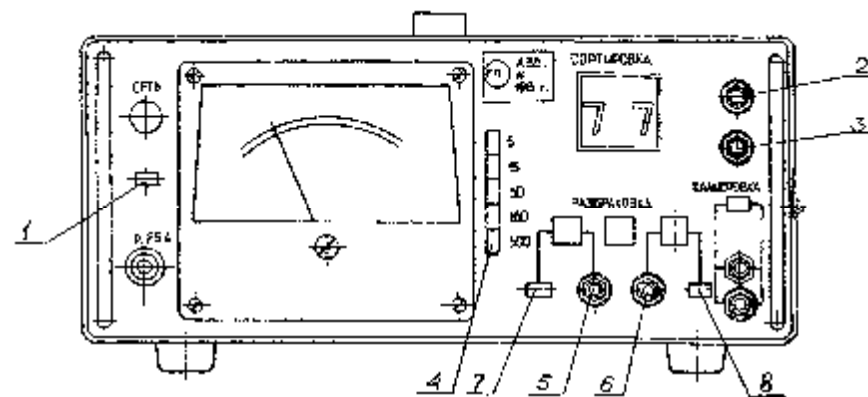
Портативный прибор приемочного контроля ПППК-А35
